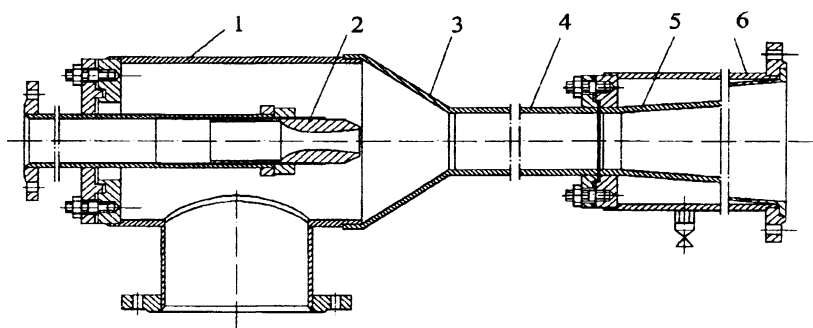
Схема пароструйного компрессора: 1 – приемная камера; 2 – рабочее сопло; 3 – переходной патрубок от приемной камеры к камере смешения; 4 – камера смешения; 5 – коническая вставка диффузора; 6 – цилиндрический корпус диффузора
